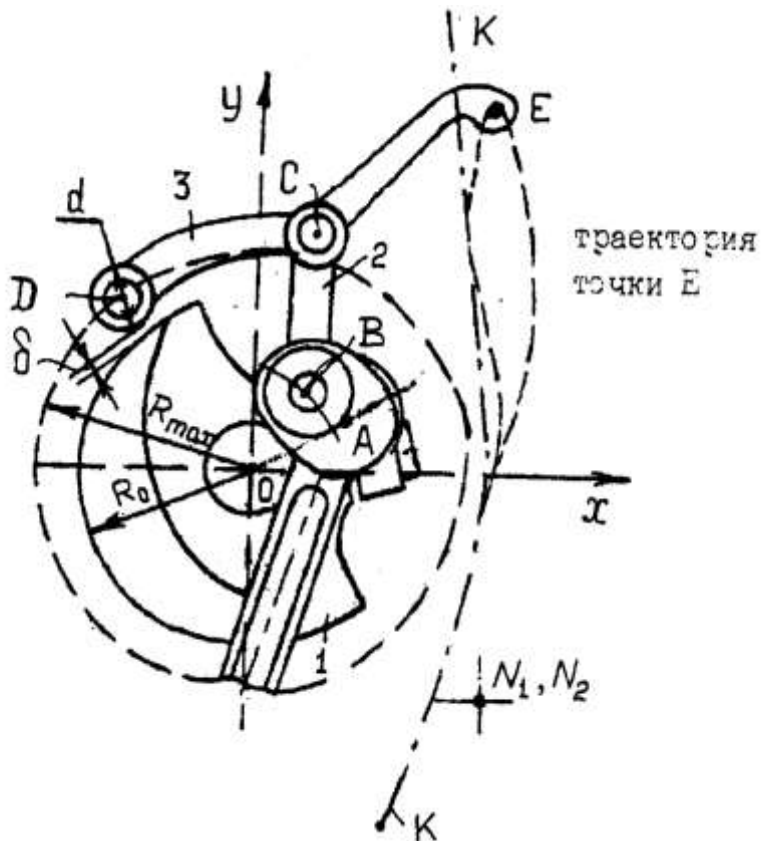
Конструктивная схема механизма нитепритягивателя: 1 – кривошип; 2 – нитепритягиватель; 3 – коромысло; O, A, B, C, D – центры шарниров; E – центр отверстия для заправки нитки
